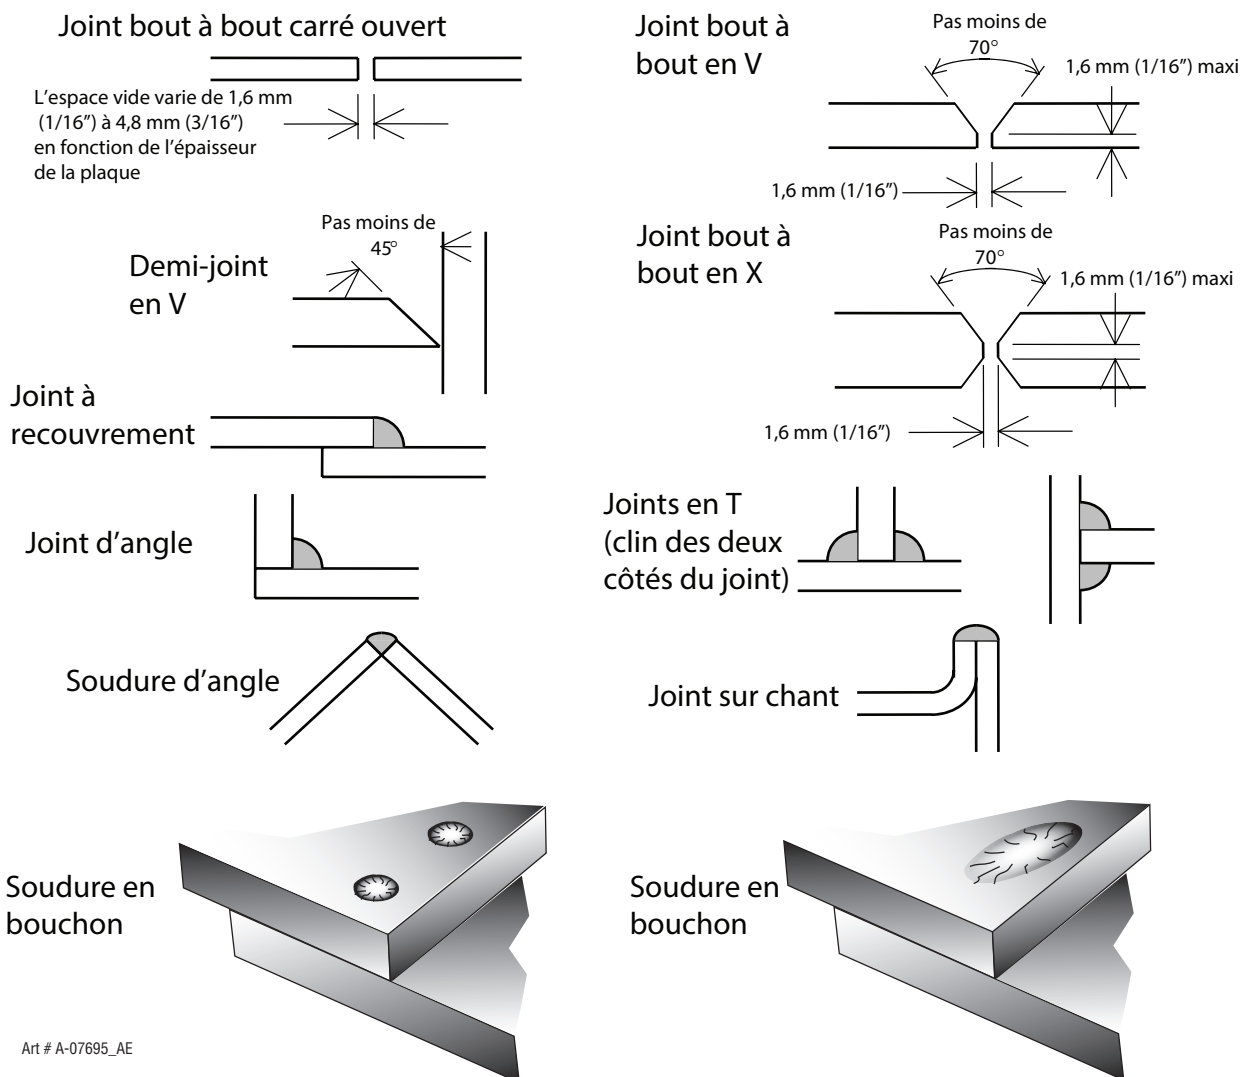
Modèles types de joints pour le soudage à l'arc
